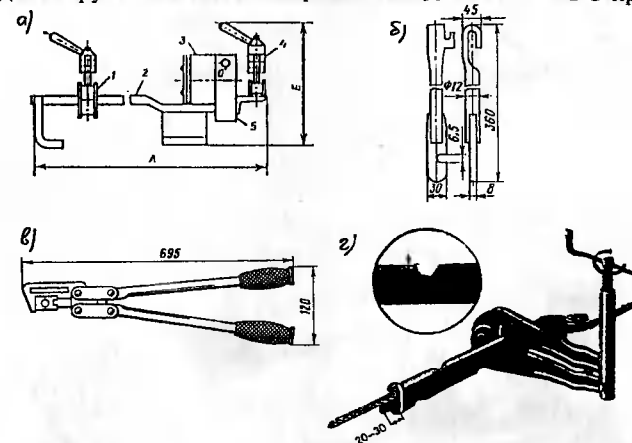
Приспособление для скручивания трубчатых соединителей (а); специальный ключ (б), клещи типа МИ-248-АК для обжатия трубчатых соединителей (в); клещи для обжатия трубчатых соединителей (г):
